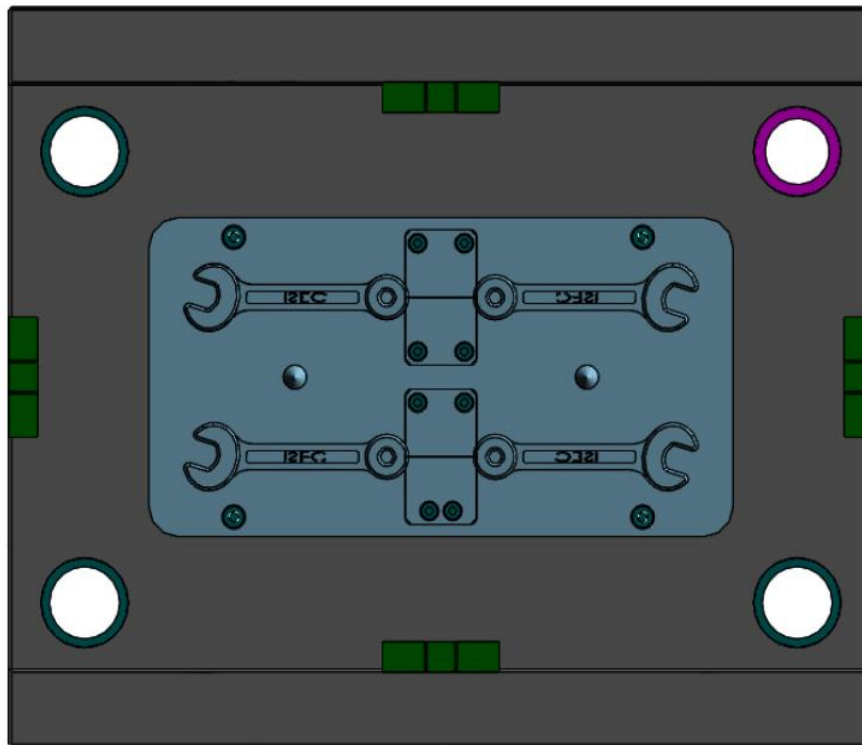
Lado da extração do molde com os posições de injeção.
